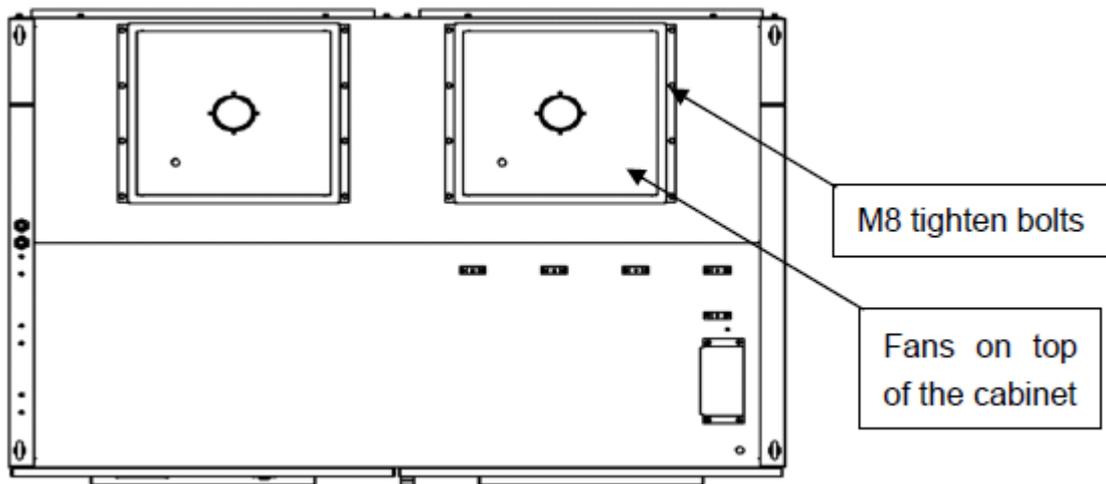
Схема установки вентилятора на верхней части шкафа.
